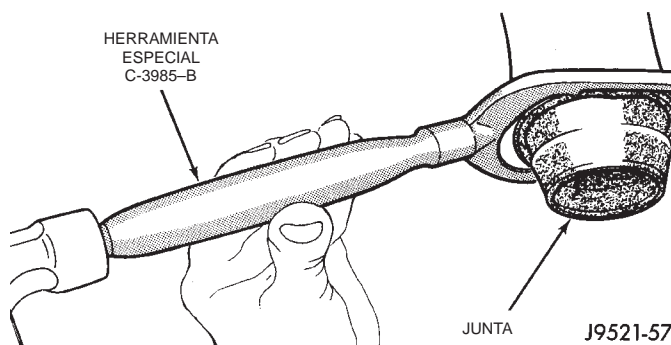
Desmontaje de la junta del estribo del retenedor de cojinete trasero
